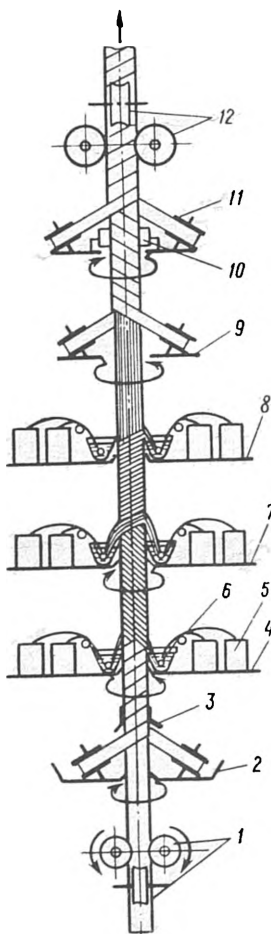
Схема вертикальной установки для изготовления труб из стеклопластиков:
